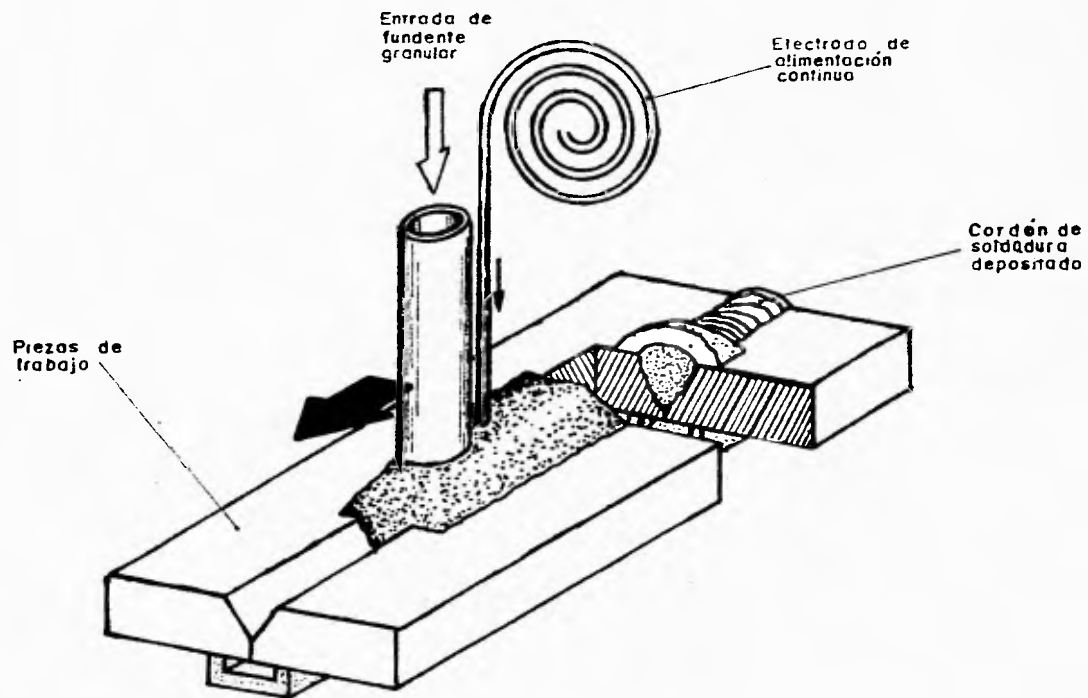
I.3. Soldadura por arco sumergido (SAW)
